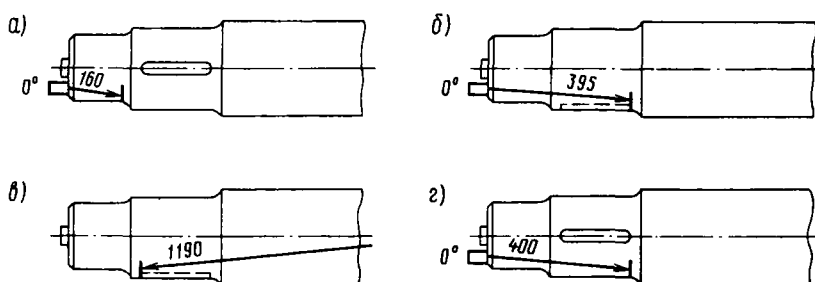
Схемы и зоны контроля прямым искателем со стороны торцов главного приводного вала эскалатора ЛТ-4 в галтелях (а, в) и в шпоночной канавке (б, г)
